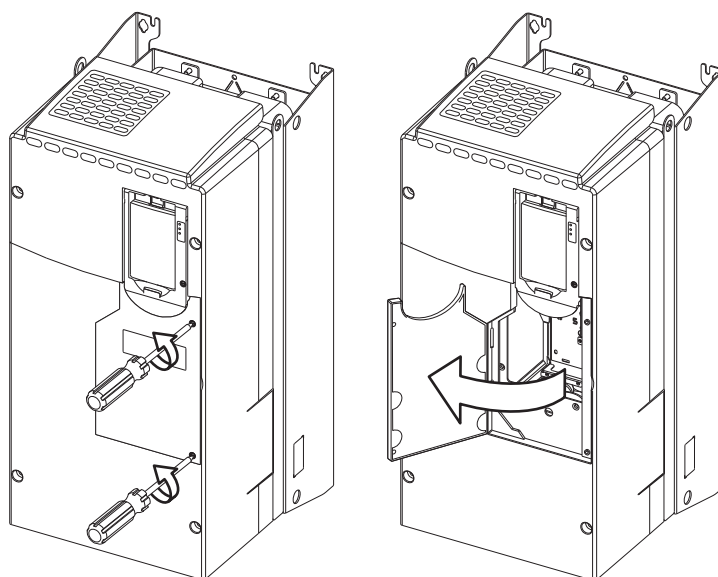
Код корпуса N (IP00, NEMA/UL Open Type), типоразмеры 6 и 7
